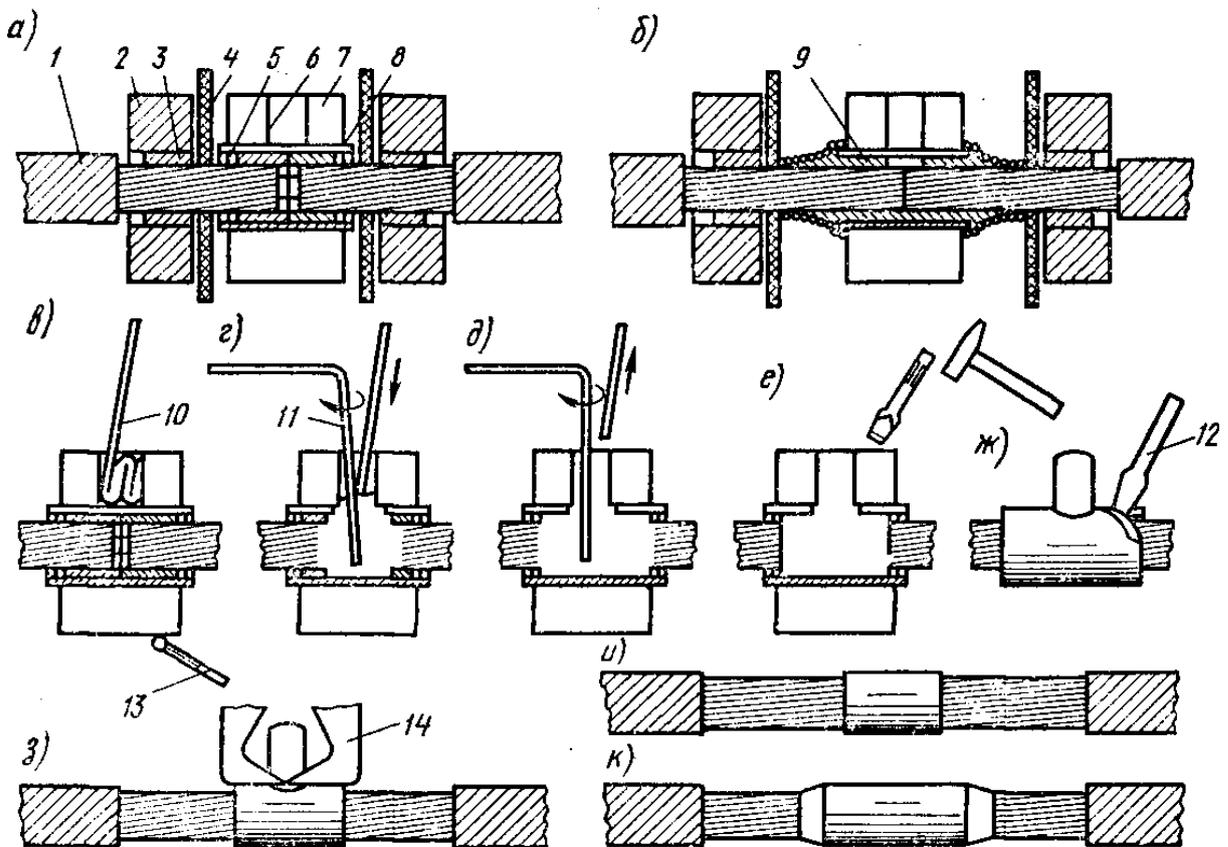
Последовательность термитной сварки встык: *а, б* - сборка под сварку соединений жил (*а* - на напряжение до 10 кВ; *б* - на 25 и 35 кВ); *в* - введение присадки в литник и поджигание муфеля; *г, д* - перемешивание расплава и добавка присадки; *е* - скалывание остывшего муфеля; *ж* - удаление кокиля; *з* - скусывание остывшего муфеля; *и, к* - готовое соединение жил (*и* - напряжение до 10 кВ; *к* - на 25 и 35 кВ); *1* - жила провода или кабеля; *2* - охладитель; *3* - вкладыш охладителя; *4* - асбестовый экран; *5* - уплотнение из асбестового шнура; *6* - алюминиевый колпачок (втулка); *7* - муфель патрона; *8* - стальной
